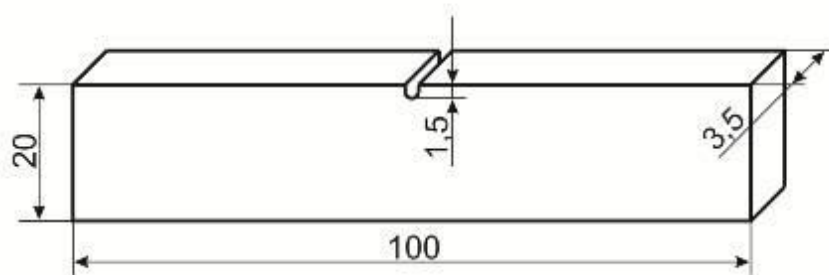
Образец для испытаний по схеме ударно-циклического изгиба
